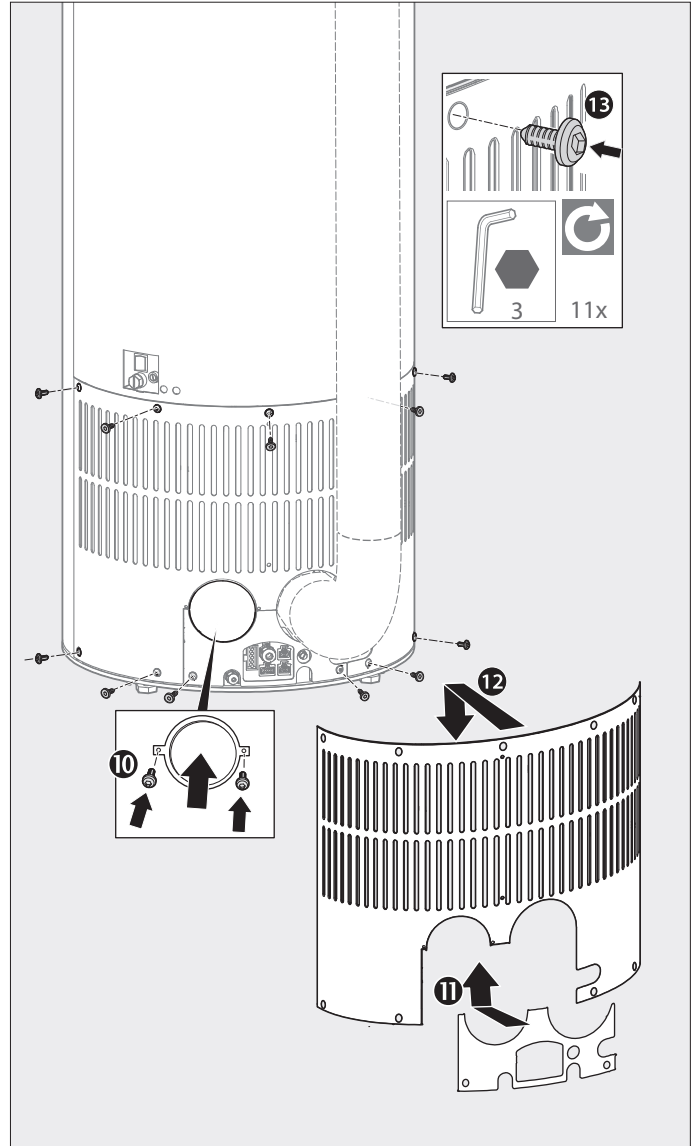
Monter la paroi arrière et le clapet fourni
